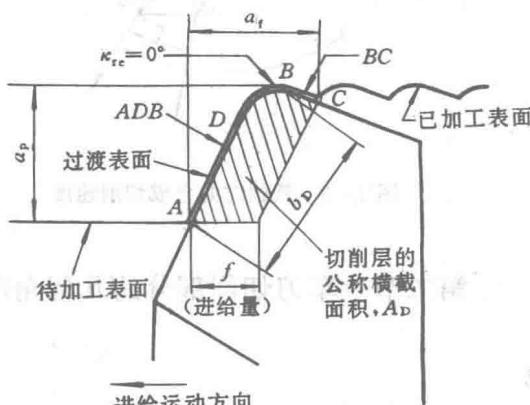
切削时的切削层尺寸——切削层尺寸平面上的视图
